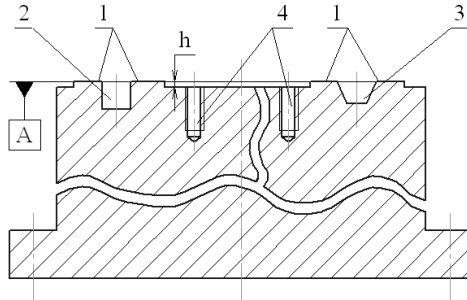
Конструкция станины станка для установки монолитных сменных направляющих
